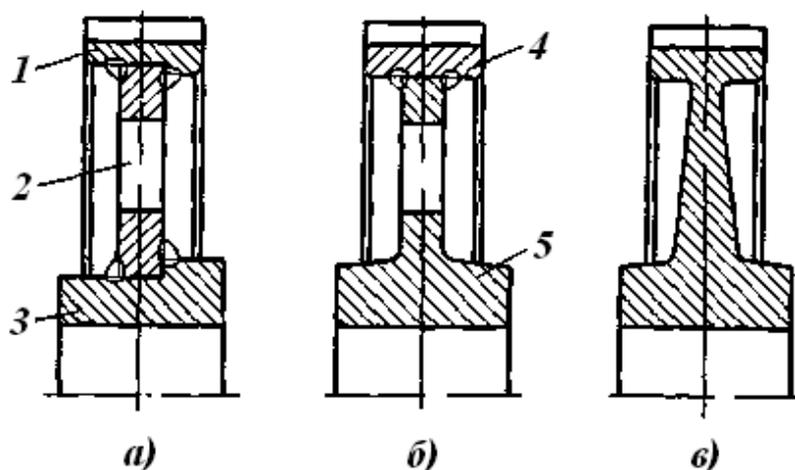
Конструктивные варианты заготовки шестерни:
